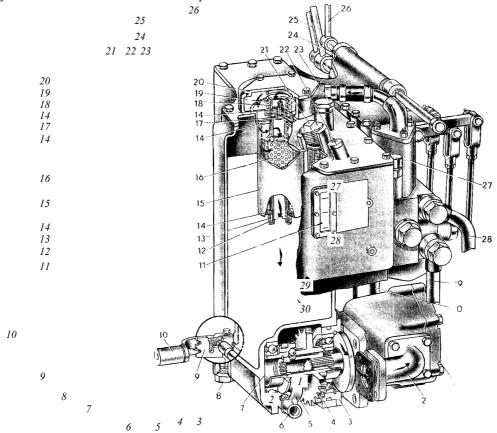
Масляный бак, фильтр и гидроагрегаты трактора МТЗ-100: 1 – гидронасос; 2 – всасывающий патрубок; 3 – стакан с подшипником; 4 – шестерня привода насоса; 5 – вилка включения; 6 – вал управления приводом насоса; 7 – бак для масла (корпус гидроагрегатов); 8 – пробка отверстия слива масла; 9 – пластина фиксатора рычага; 10 – рукоятка включения и выключения насоса; 11 – смотровое окно-указатель уровни масла; 12 – труба слива очищенного масла; 13 – поджимная пружина; 14 – уплотнительное кольцо; 15 – корпус фильтра; 16 – фильтрующий элемент; 17 – клапан фильтра; 18 – втулка; 19 – пружина фильтра; 20 – крышка фильтра; 21 – пробка заливной горловины; 22 – предохранительный клапан ГОРУ; 23 – сапун; 24 – рычаг управления правыми боковыми выводами гидросистемы; 25 – рычаг управления правыми задними выводами гидросистемы; 26 – рычаг управления левыми задними выводами гидросистемы; 27 – трехзолотниковый распределитель; 28 – труба, соединяющая распределитель с полостью опускания основного гидроцилиндра; 29 – промежуточный маслопровод;
